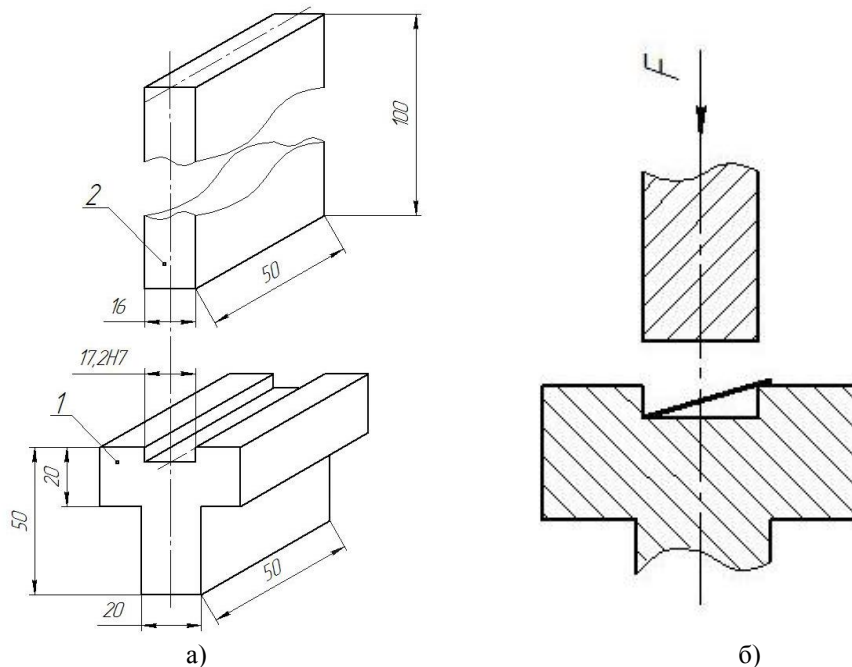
Креслення штампу для гнуття відбортовки і схема застосування
